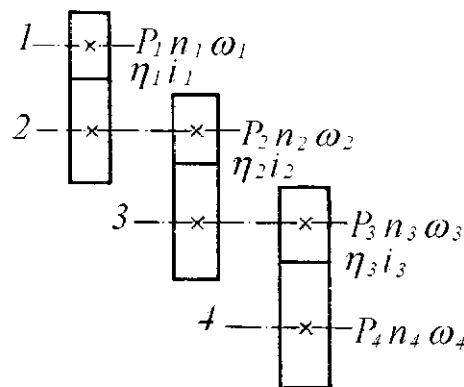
Схема передачи с последовательно соединенными звеньями
